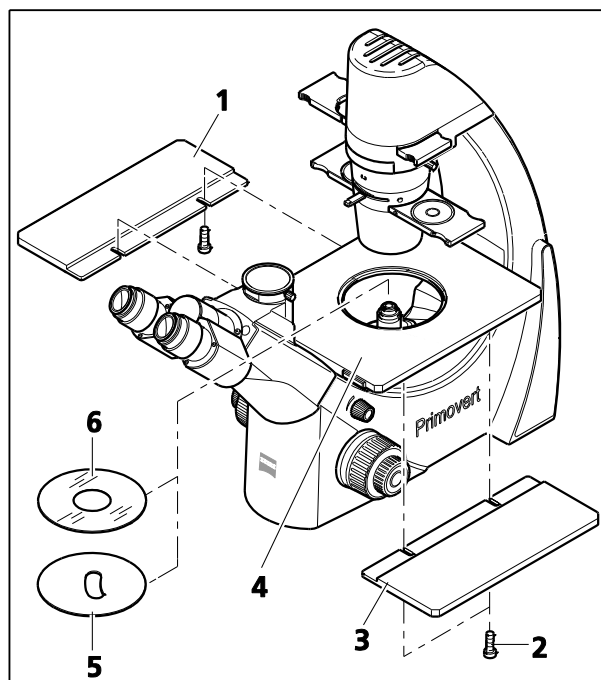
Installation des inserts de platine et fixation des plaques d'agrandissement de la platine
